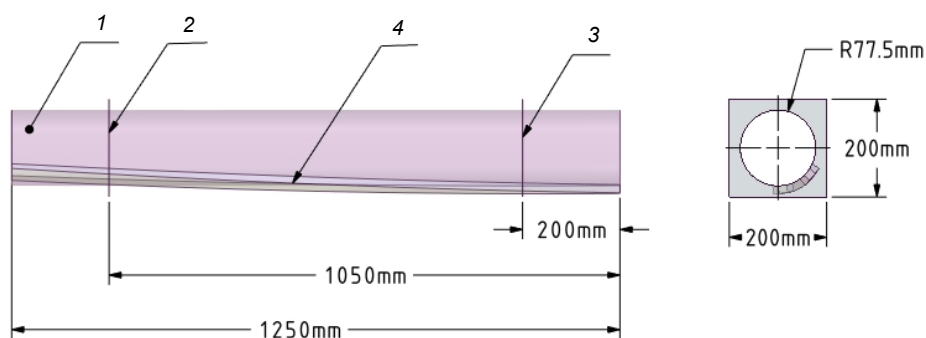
Конструкция трубчатой направляющей: 1 – труба; 2, 3 – диафрагмы; 4 – паз
